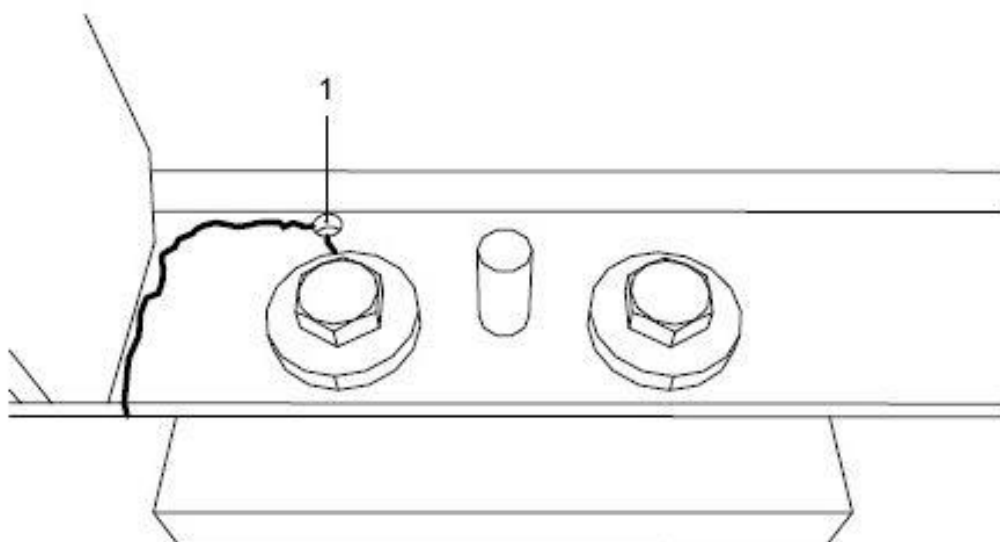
Taladrado de finales de fisuras (paso 1).
